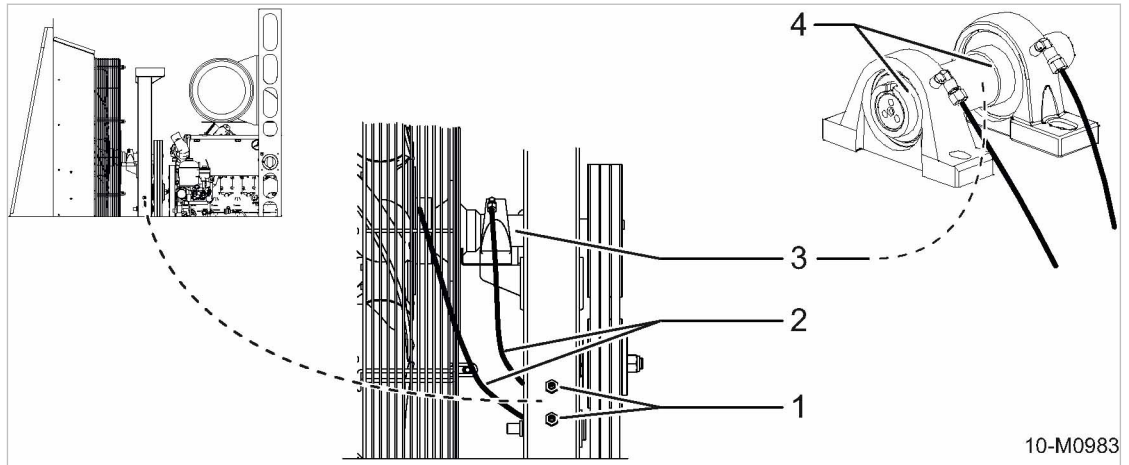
Engrasar los cojinetes del árbol de ventilador
